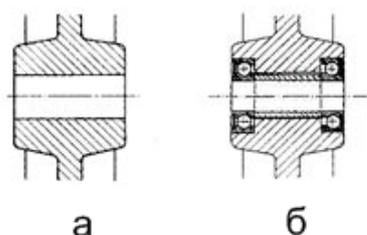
Колесные опоры: а) на подшипниках скольжения; б) на подшипниках качения
